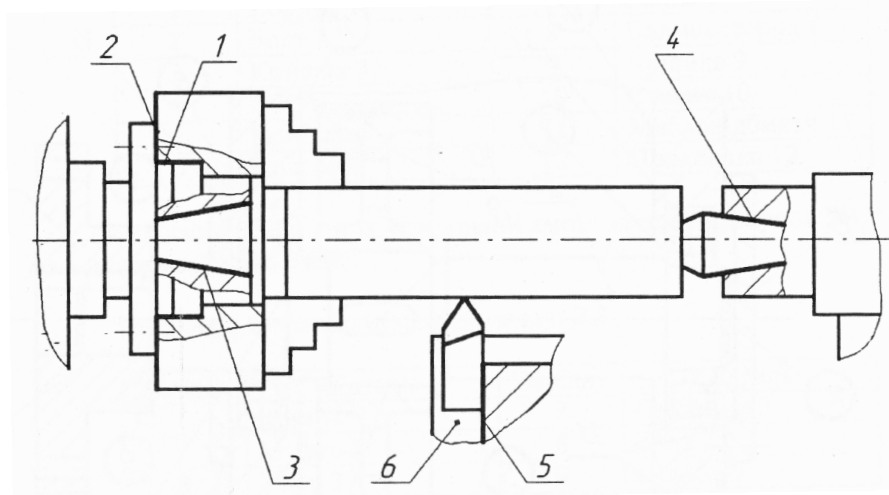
Виконавчі поверхні токарного верстата
